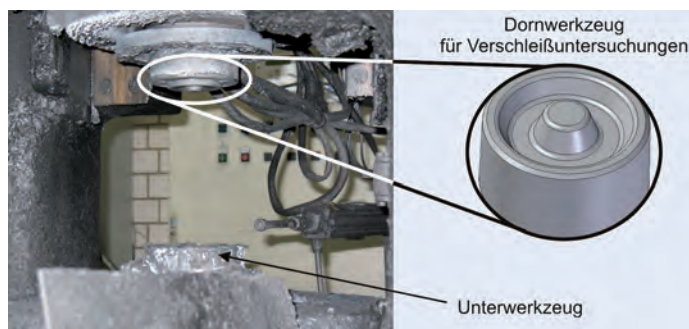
Werkzeugsystem für Verschleißuntersuchungen.
